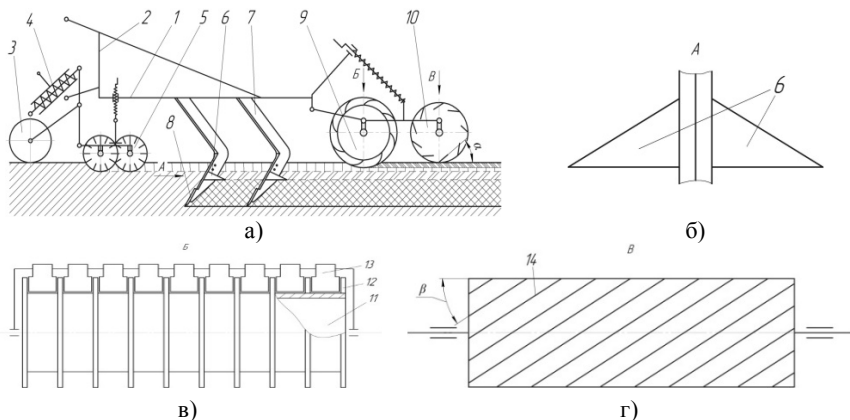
Схема комбинированный почвообрабатывающий агрегат для формирования влагосберегающего и влагонакопительного слоя почвы на склоновых землях: а) вид агрегата сбоку; б) вид А; в) вид Б; г) вид В
